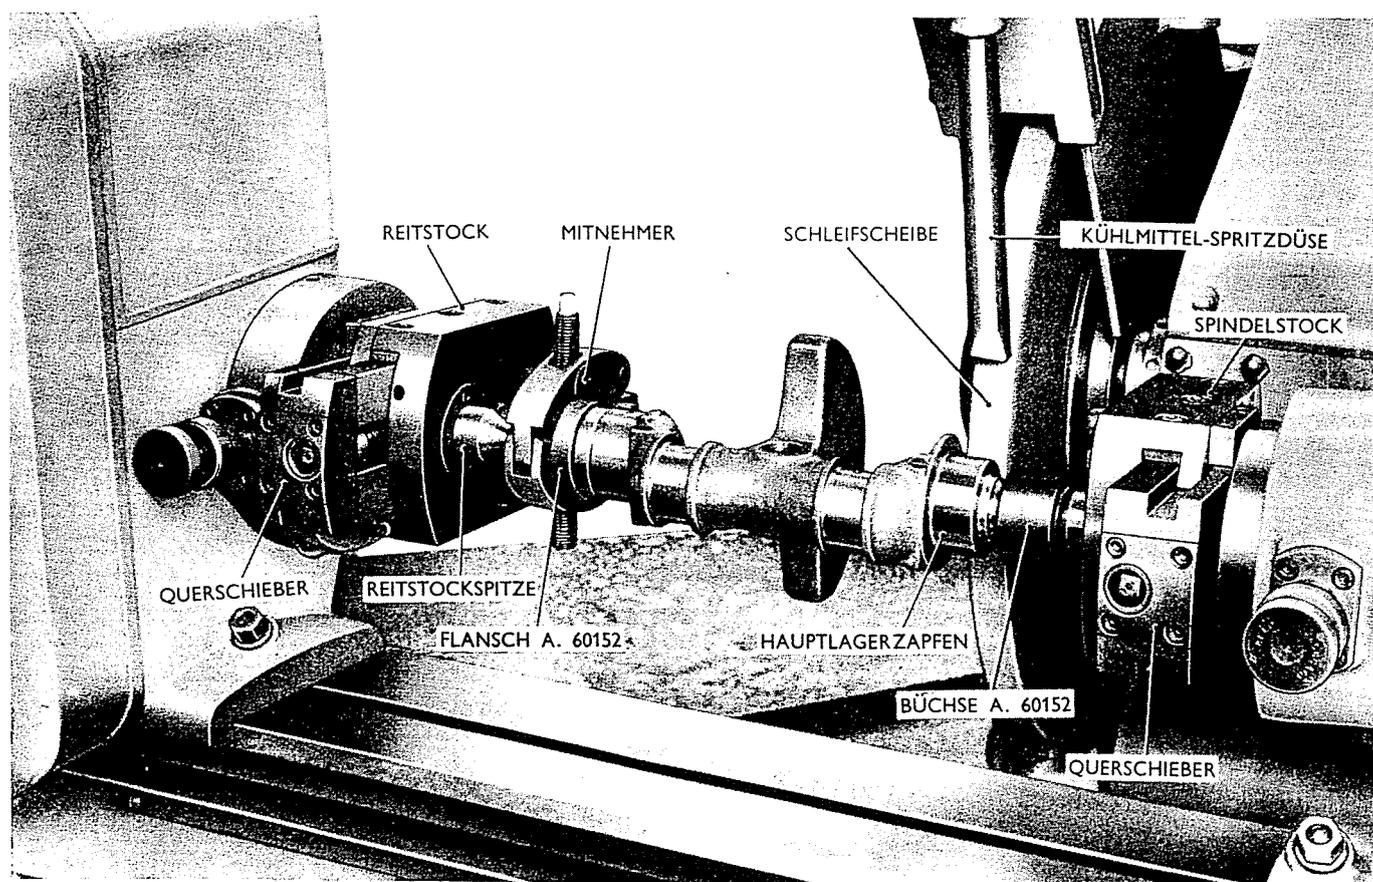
Schleifen der Hauptlagerzapfen auf der Schleifmaschine.
